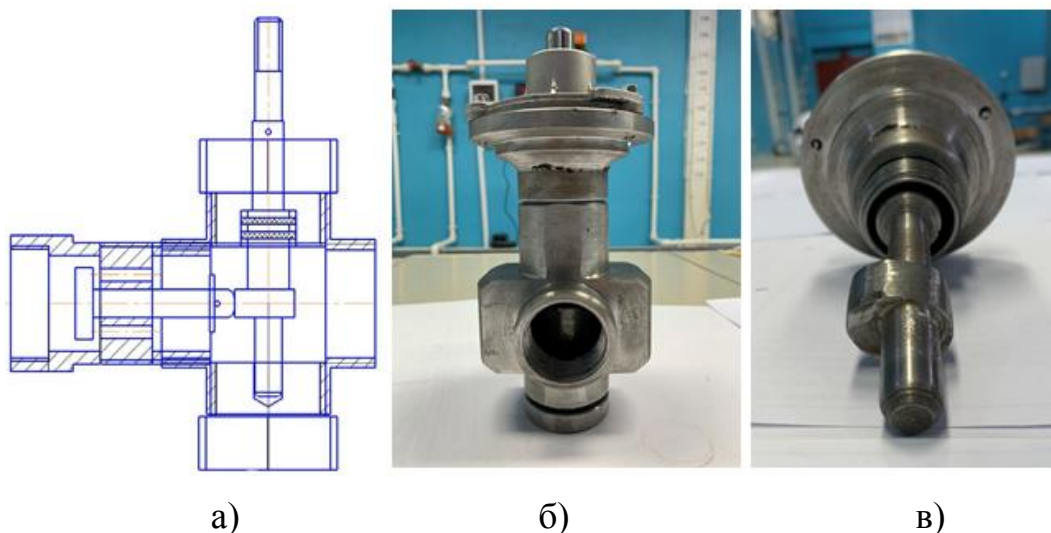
Схема ударного узла (а), внешний вид ударного узла в сборе (б), внешний вид штока с кулачком закрепленном в помпе (в)
